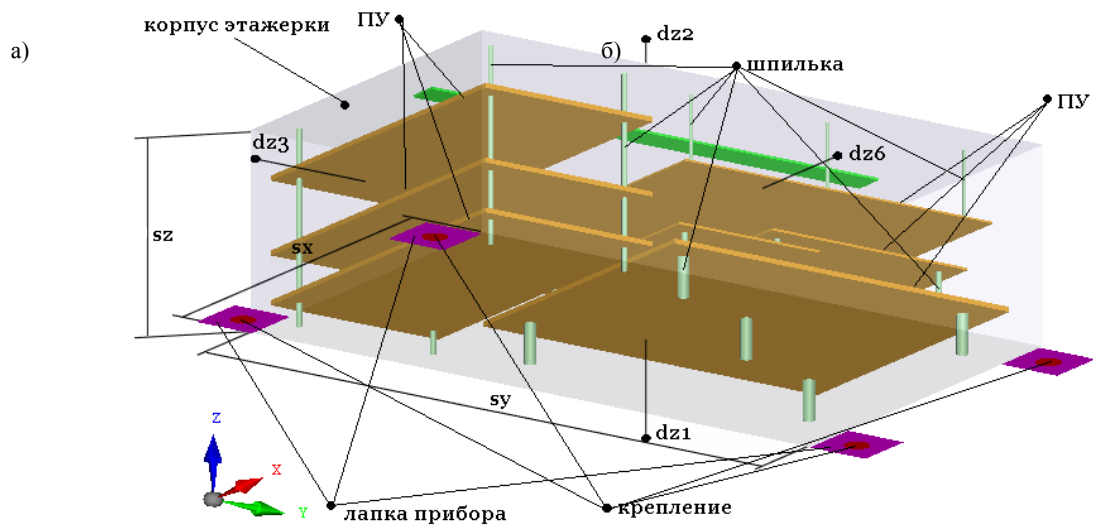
Внешний вид несущей конструкции блок сложного этажерочного типа (а – вид спереди, б – вид сзади)
